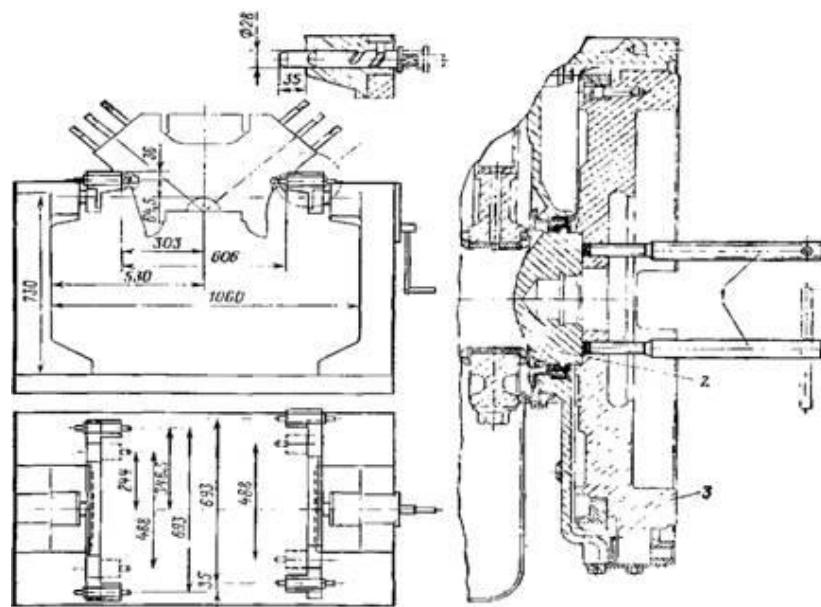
Стенд для ремонта двигателя Рисунок 1.6 – Воротки для снятия маховика
